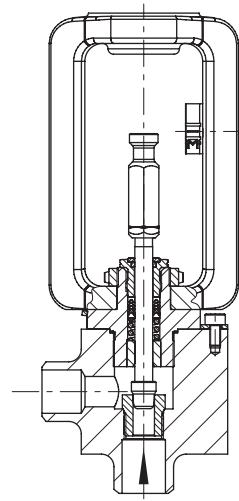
Válvula para altas presiones Tipo 3252 de ángulo con extremos para soldar
